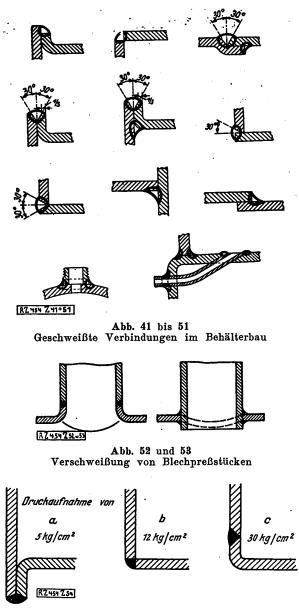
• Eckschweißungen an Ölbehältern
